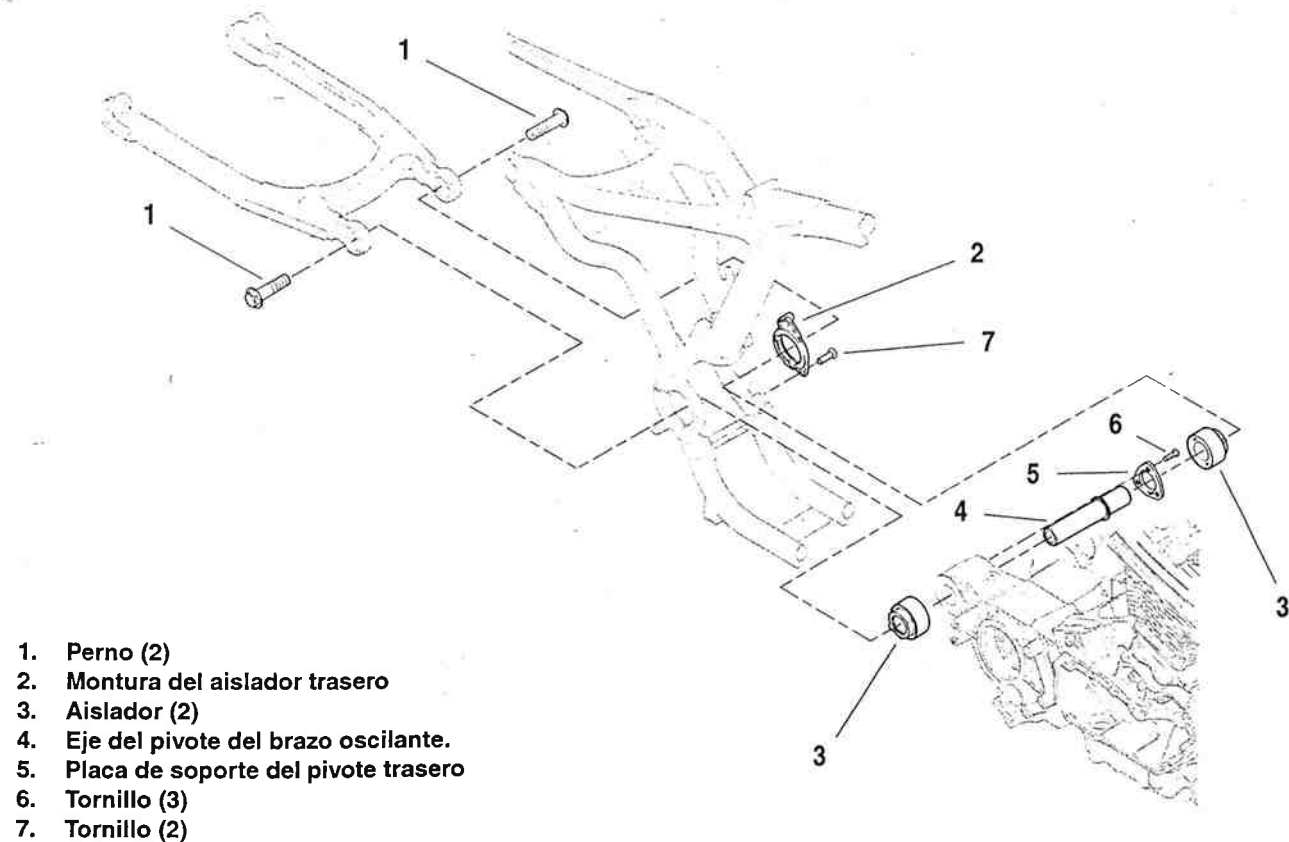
Conjunto del soporte trasero del motor/aislador
